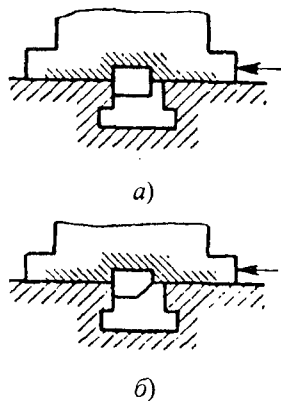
Конструкции шпонок, обеспечивающие повышение точности установки приспособления:
